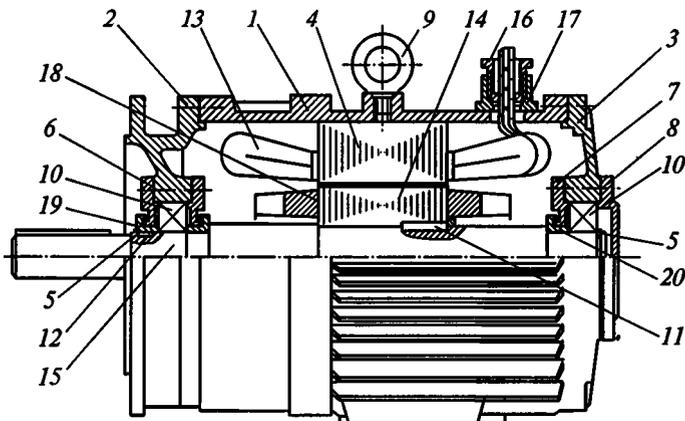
Асинхронный двигатель типа АЭВ160S2У2:
